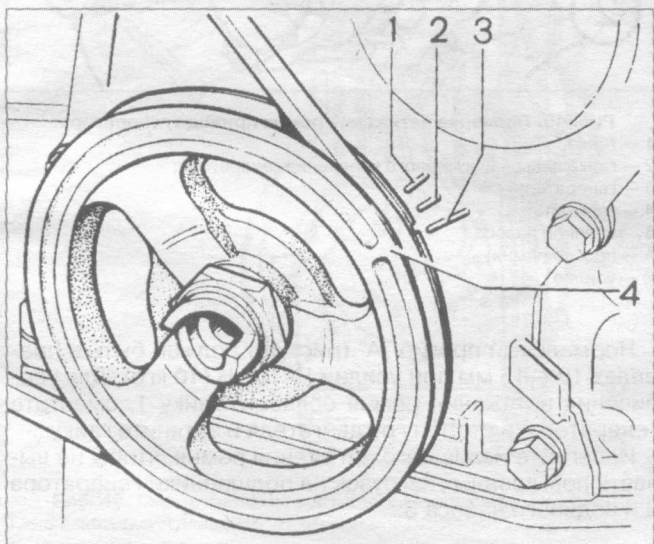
Метки на шкиве и крышке привода механизма газораспределения:
